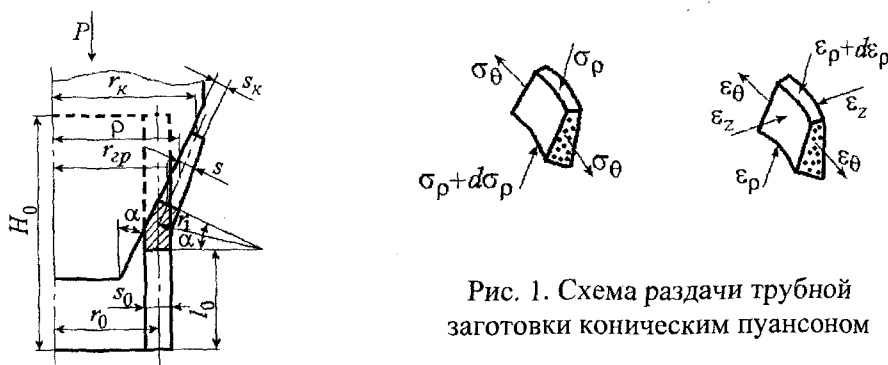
Схема раздачи трубной заготовки коническим пуансоном
